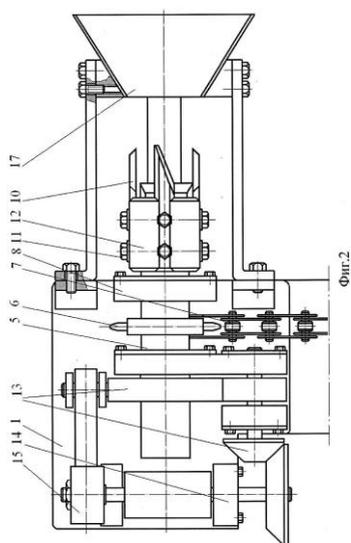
Устройство для заготовки хвойной лапки (вид сверху)
